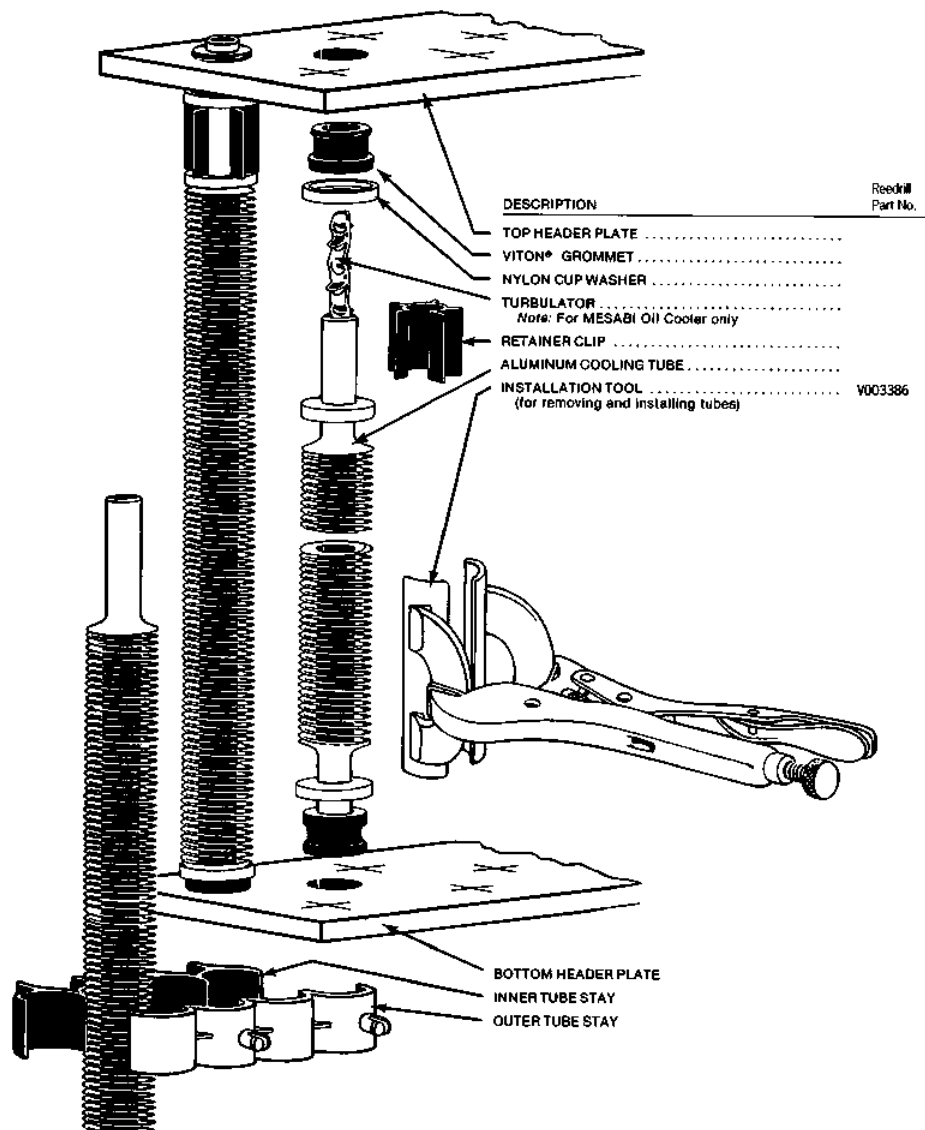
Outil de montage pour tube rond (radiateur L&M)
